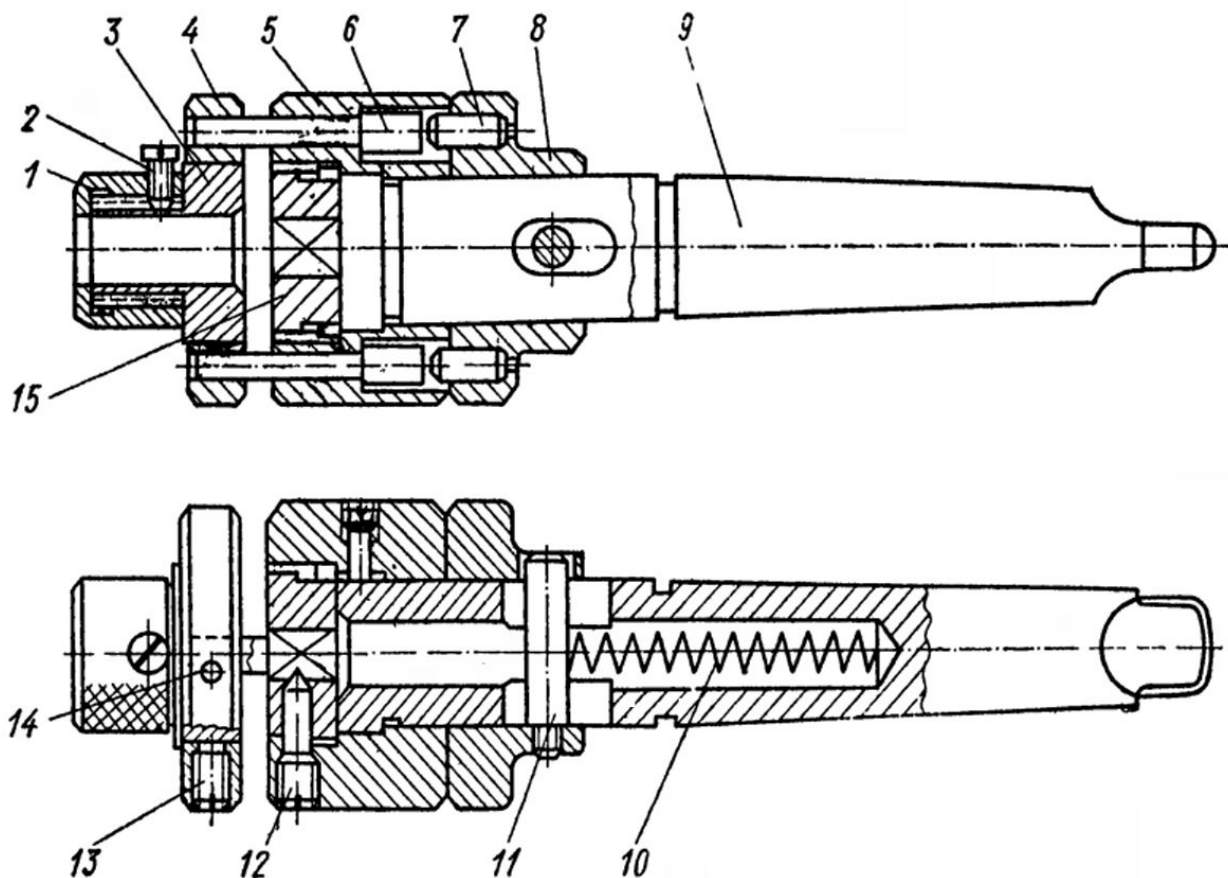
Приспособление с предохранительным патроном для нарезания резьбы метчиками
